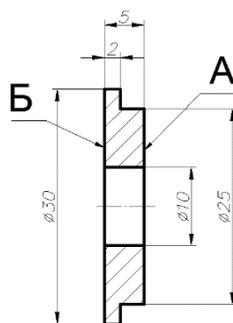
Конструктивное исполнение металлического образца имплантата
